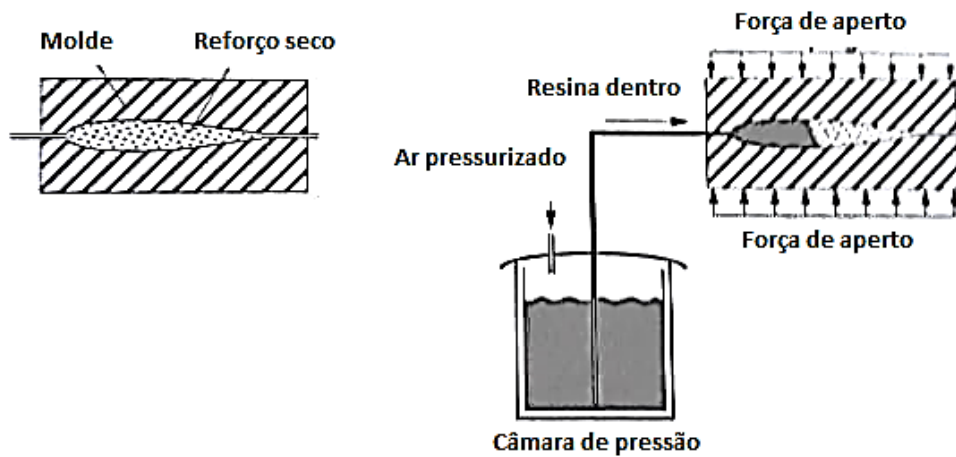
Esquema em detalhe da técnica de moldação de resina por transferência. Adaptado de [64]
